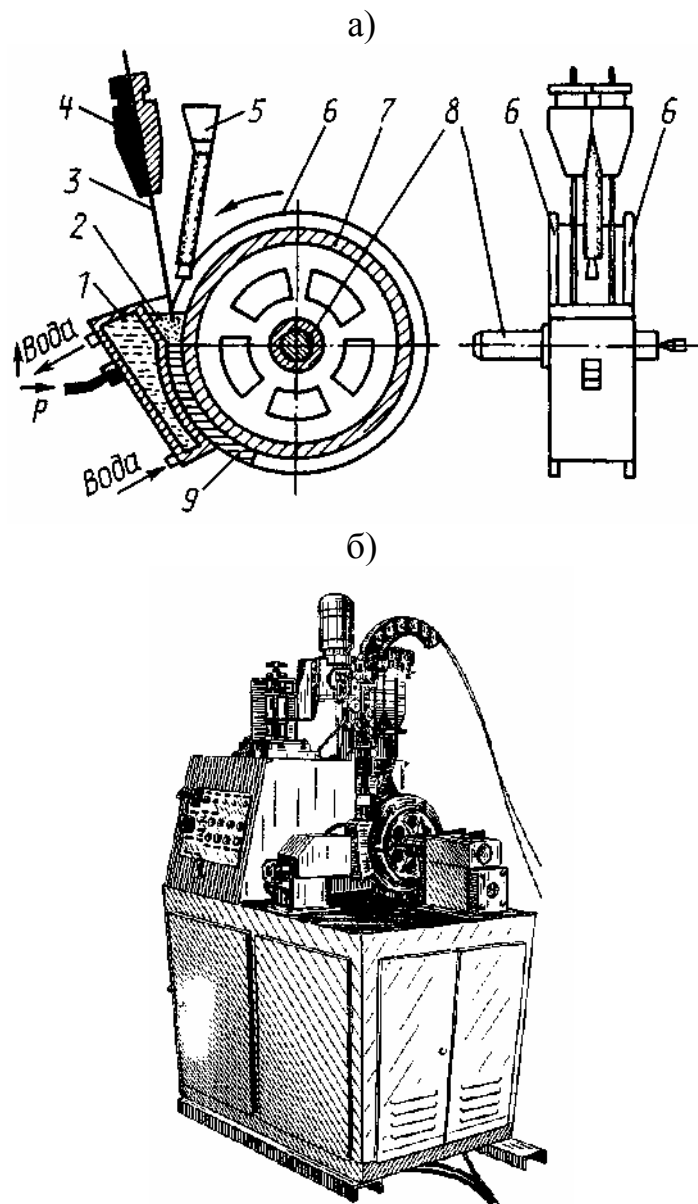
Установка ОКС-7755 ГосНИТИ для электрошлаковой наплавки катков и шкивов: а) – схема процесса; б) – общий вид; 1 – кристаллизатор; 2 – шлаковая ванна; 3 – электрод; 4 – мундштук; 5 – дозатор легирующих добавок; 6 – габаритные диски; 7 – восстанавливаемая деталь; 8 – оправка; 9 – покрытие
